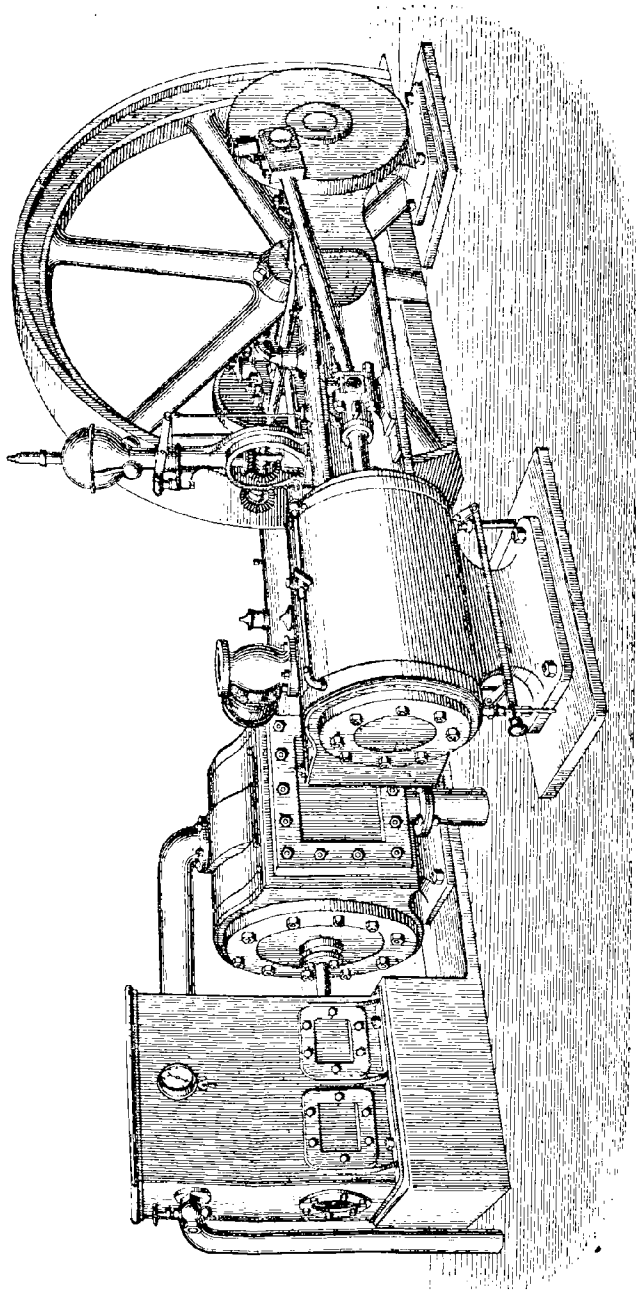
Machine horizontale de Davy et Paxman (vue perspective).
